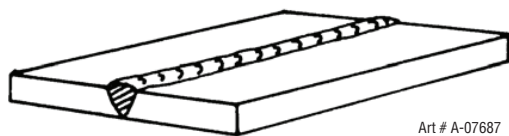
Soudure à plat, bout à bout depuis le haut
